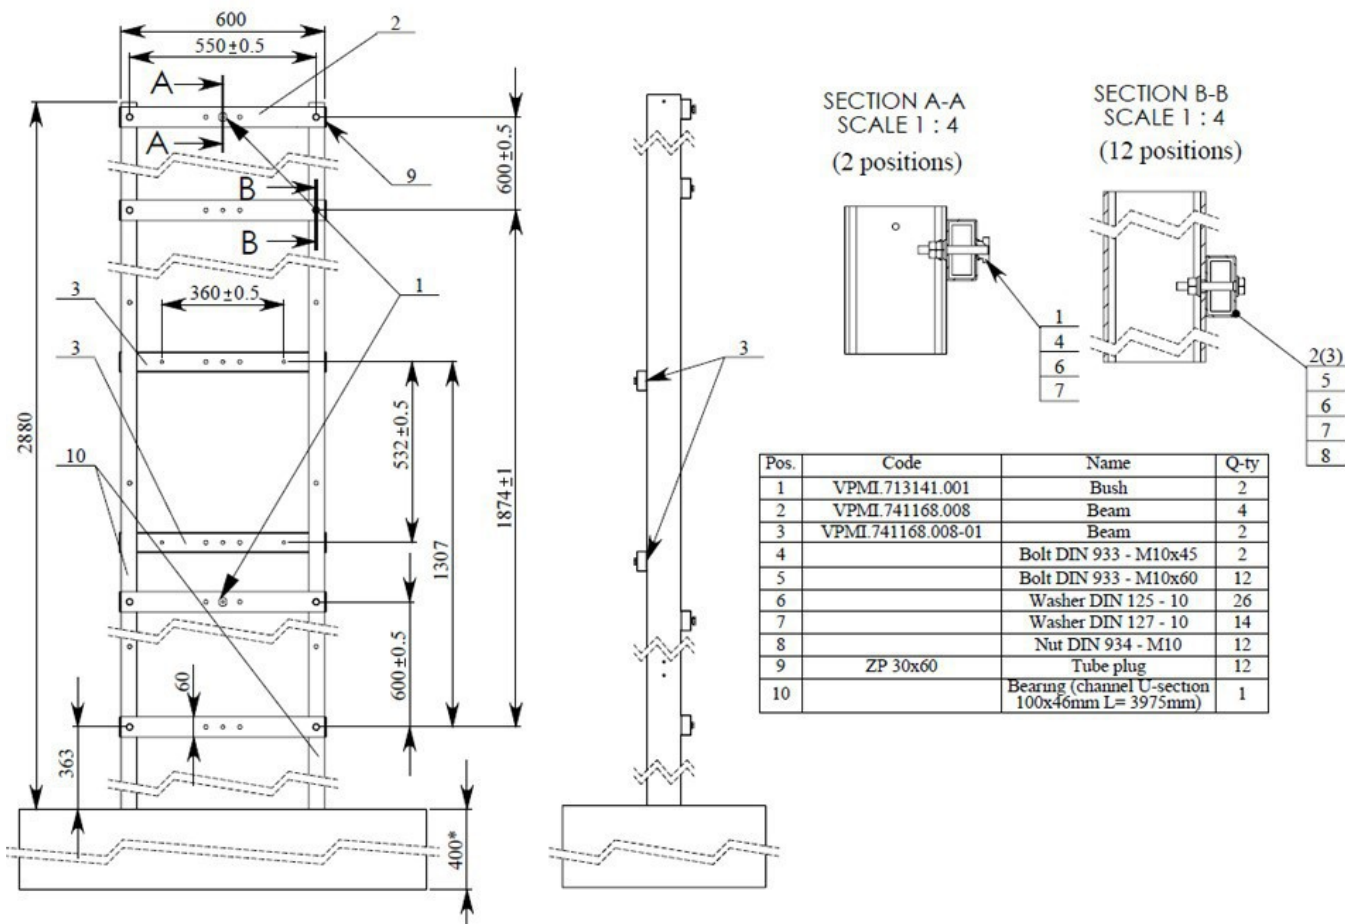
Montaje de vigas y casquillos en el pilar principal de PoliGate Light G4
